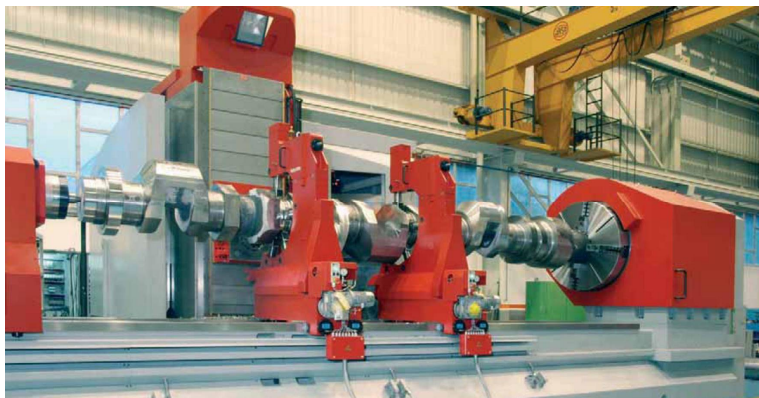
Унікальний токарний верстат для обточування шийок колінчастих валів
